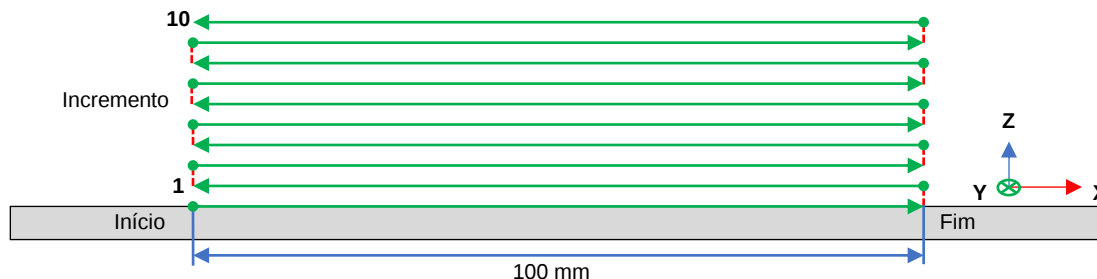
Representação esquemática da trajetória utilizada para construção das paredes.
